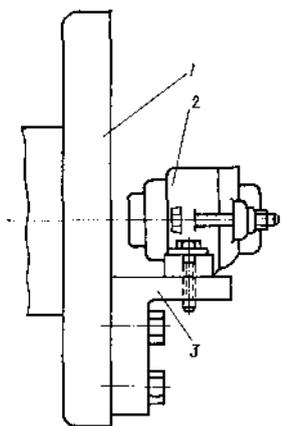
Закріплення корпусу підшипника для розточування на токарному верстаті:
